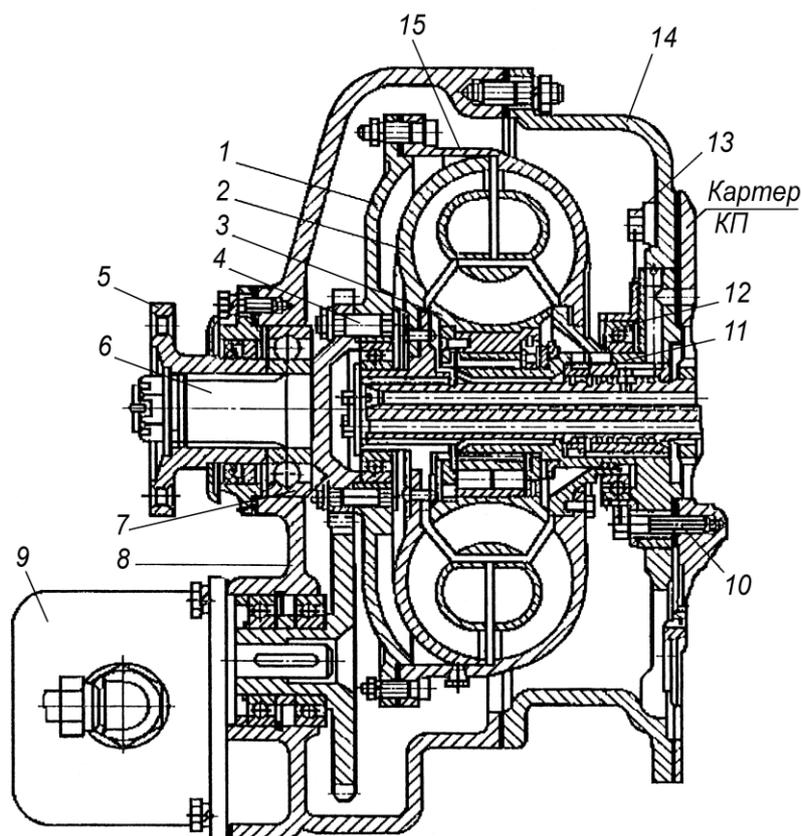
Гидротрансформатор: 1 – крышка; 2 – турбинное колесо; 3 – реакторное колесо; 4, 10, 13 – болты; 5 – фланец; 6 – входной вал; 7, 12 – подшипники; 8 – картер; 9 – насос гидросистемы ГМП; 11 – цапфа; 14 – переходный картер; 15 – насосное колесо
